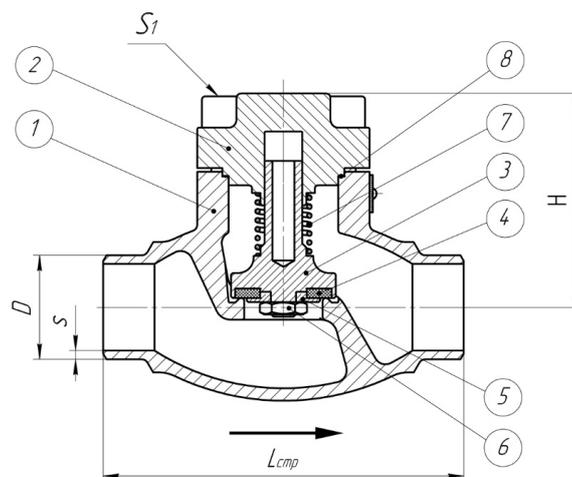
Конструкция клапана обратного тип 7724-0440-1-00
